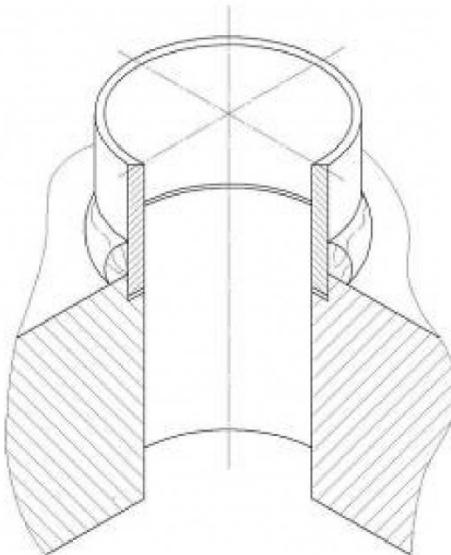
Трешины в сварном шве приварки штуцера к барабану.
